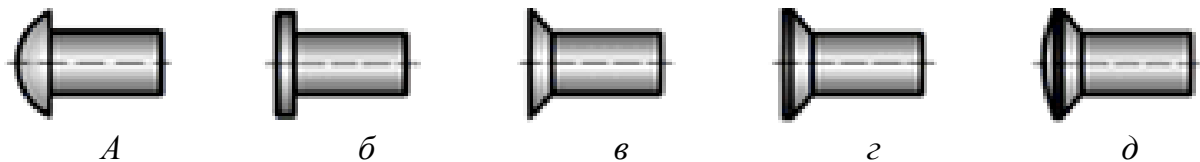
Заклепки со сплошным стержнем: *a* – с полукруглой головкой; *б* – с цилиндрической головкой; *в* – с конической головкой; *г* – с потайной головкой; *д* – с полупотайной головкой.
